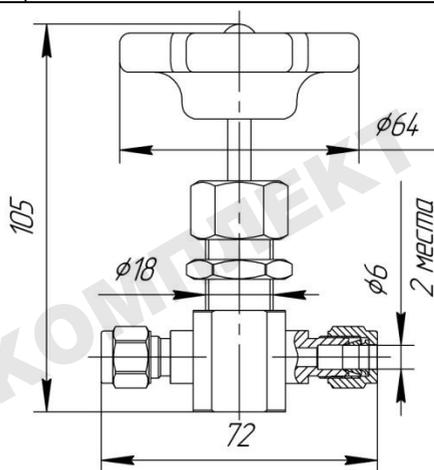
Габаритно-присоединительные размеры ВИГ250Ф-И1-М6М6М
